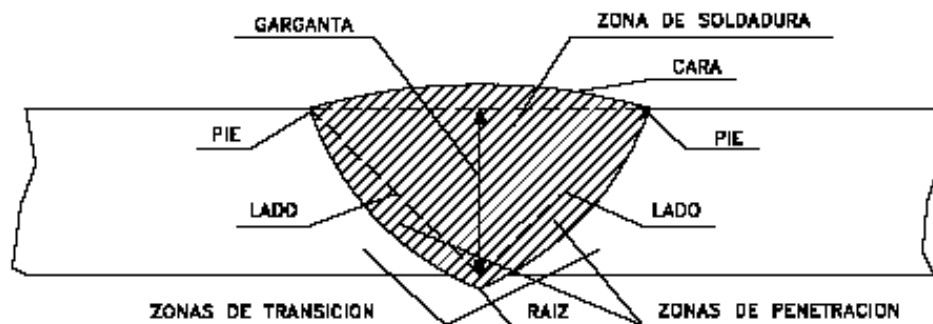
PARTES DE UN CORDON DE SOLDADURA (Ref. 4)
